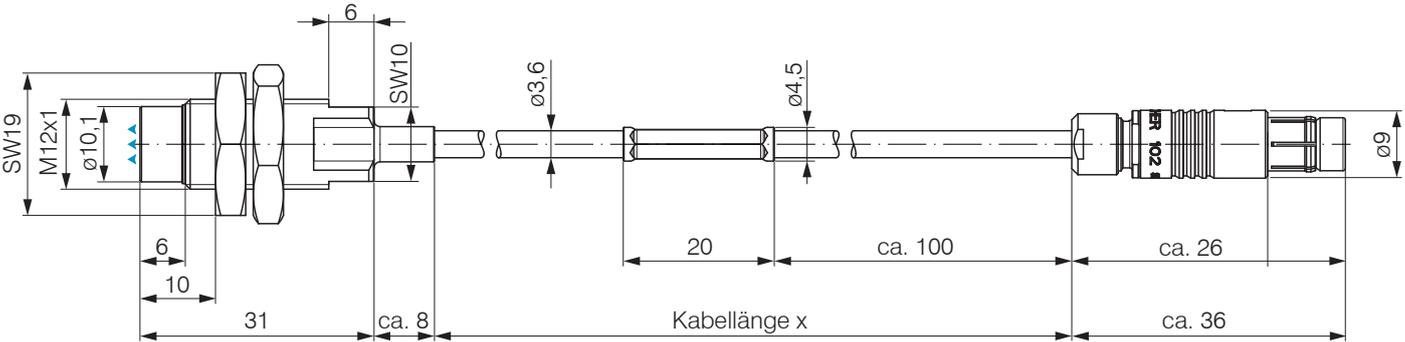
Maßzeichnung Sensoren ES-U3-C-CAX/mB0, Abmessung in mm
